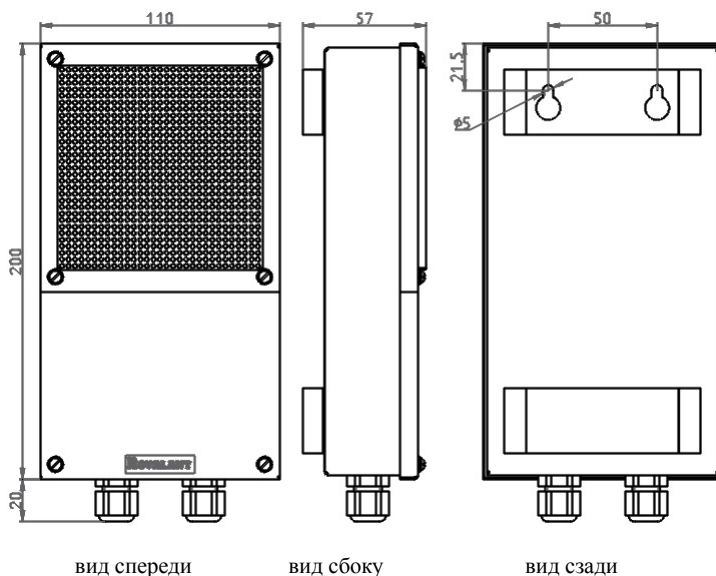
Внешний вид, габаритные и установочные размеры корпуса оповещателя
